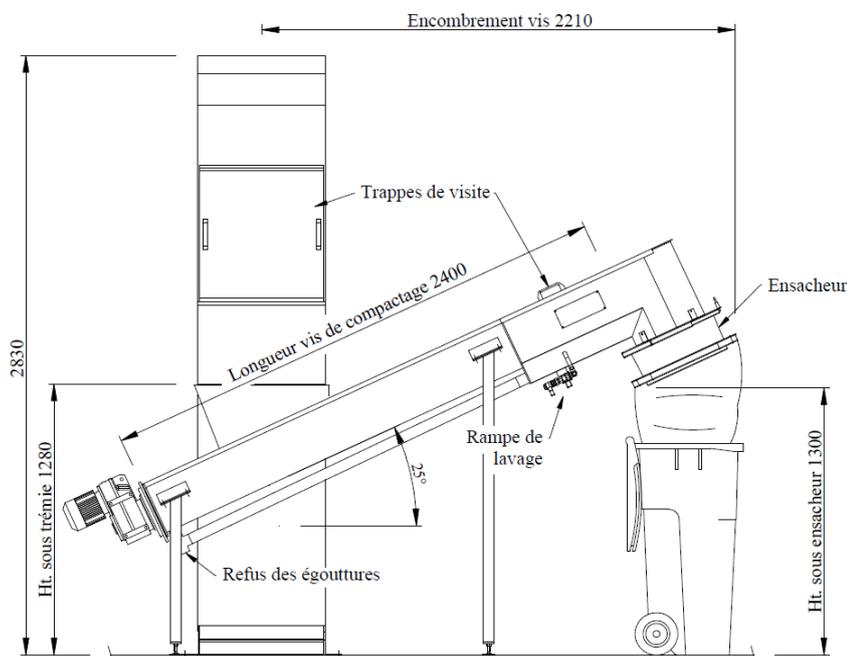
EXEMPLE D'INSTALLATION DE COMPACTAGE DES REFUS DE DEGRILLAGE ENVISAGEABLE SUR LES INSTALLATIONS EXISTANTES
